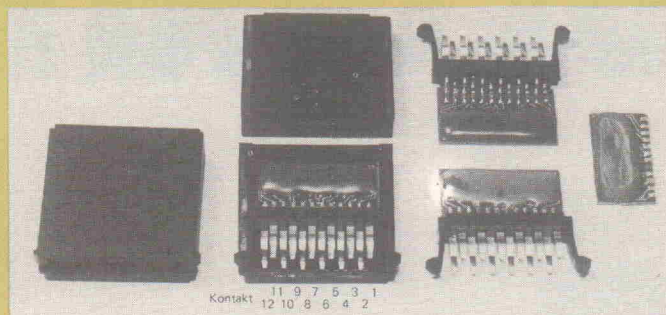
Ansicht der Memory Module von links nach rechts: geschlossenes Gehäuse, geöffnetes Modul, Leiterplatte mit Stecker, vom Stecker entfernte Leiterplatte.
